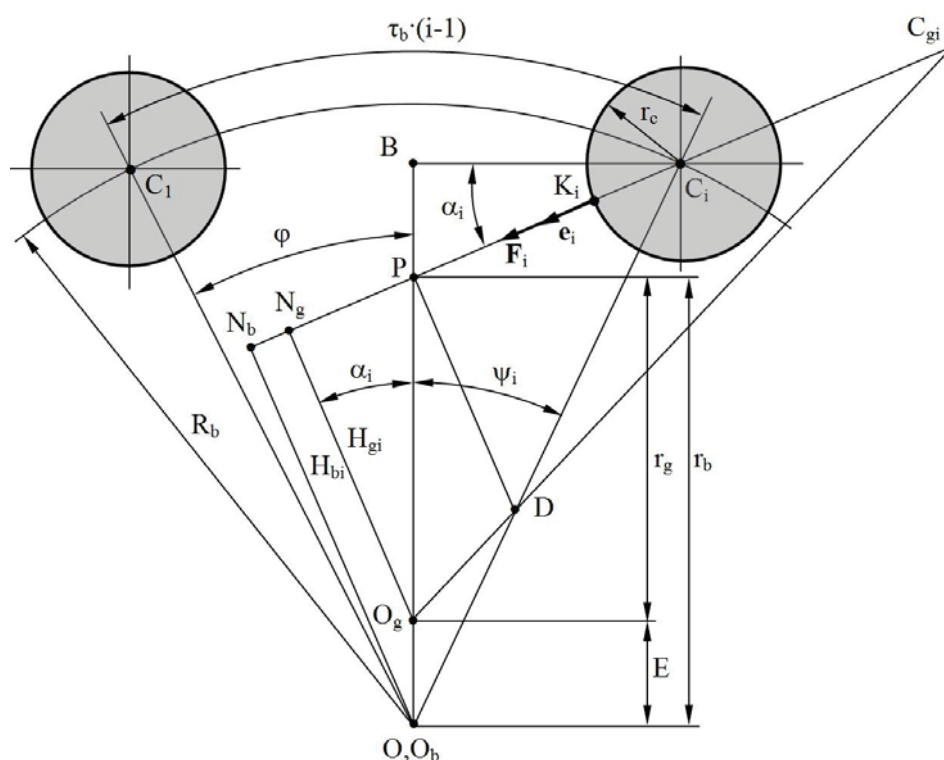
Построение Бобилье для зацепления цевки с зубом сателлита (сателлит не показан): O – центральная ось; O_b – ось колеса; O_g – ось сателлита; P – полюс зацепления; φ – угол поворота входного вала; ψ_i – угловое положение цевки; r_b, r_g – радиусы центроид колеса и сателлита; r_c – радиус цевок; R_b – радиус окружности центров цевок; E – эксцентриситет сателлита; K_i – точка контакта; e_i – орт профильной нормали; F_i – сила в зацеплении; α_i – угол зацепления; H_{bi}, H_{gi} – плечи профильной нормали относительно оси колеса и оси сателлита; C_1, C_i – центры цевок; τ_b – шаг цевок; C_g – центр кривизны зуба сателлита; D – точка пересечения прямых, соединяющих центры кривизны сопряженных профилей и центры кривизны центроид ($C_i O_b$ и $C_g O_g$;))
